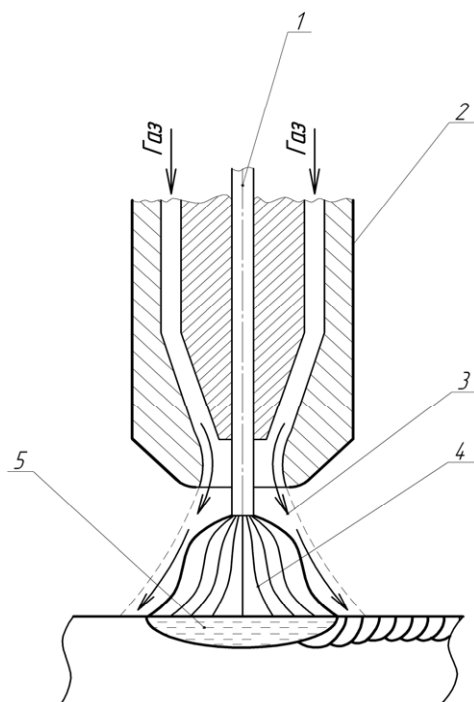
Схема наплавки в среде защитного газа: 1 – электродная проволока; 2 – сварочная горелка; 3 – атмосфера защитного газа; 4 – электрическая дуга; 5 – сварочная ванна
